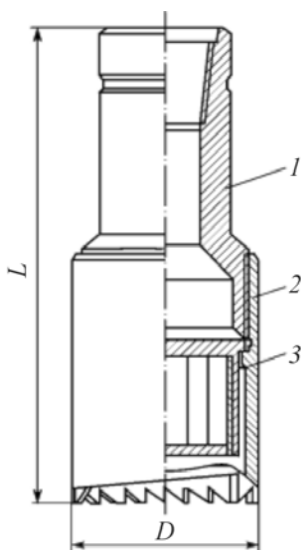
Магнитный фрезер-ловитель типа ФМ: 1 – переводник; 2 – корпус фрезера; 3 – система магнитная
